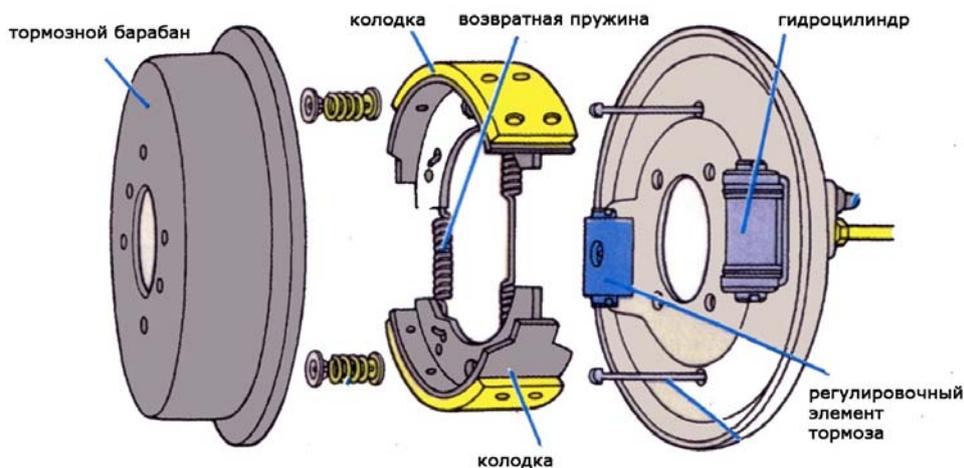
Барабанный тормозной механизм заднего колеса
